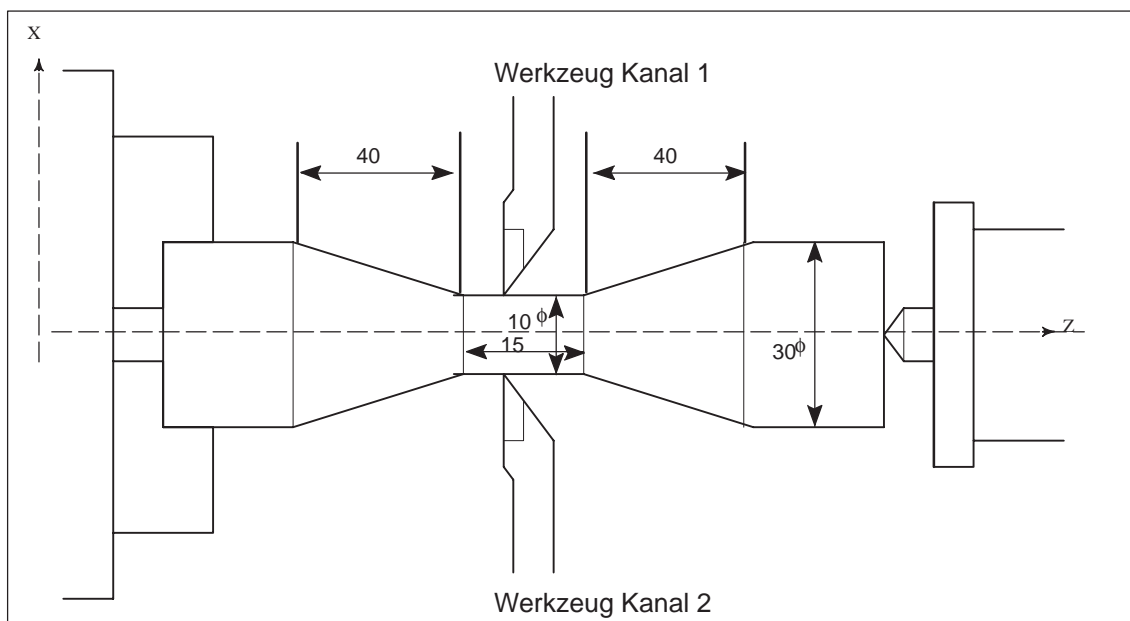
Synchrone Bearbeitung mit 2 Kanälen
